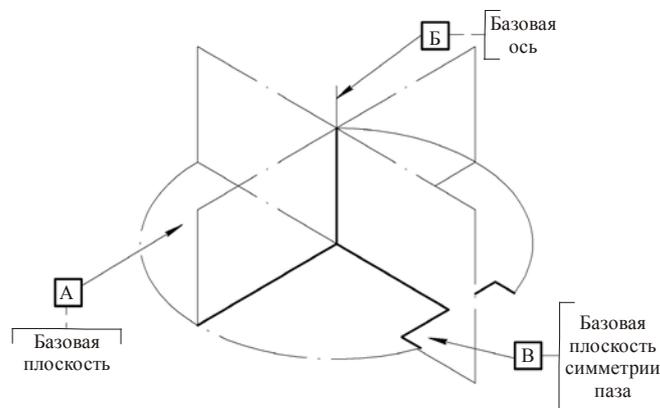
Базовая система координат для цилиндрической детали с пазом
